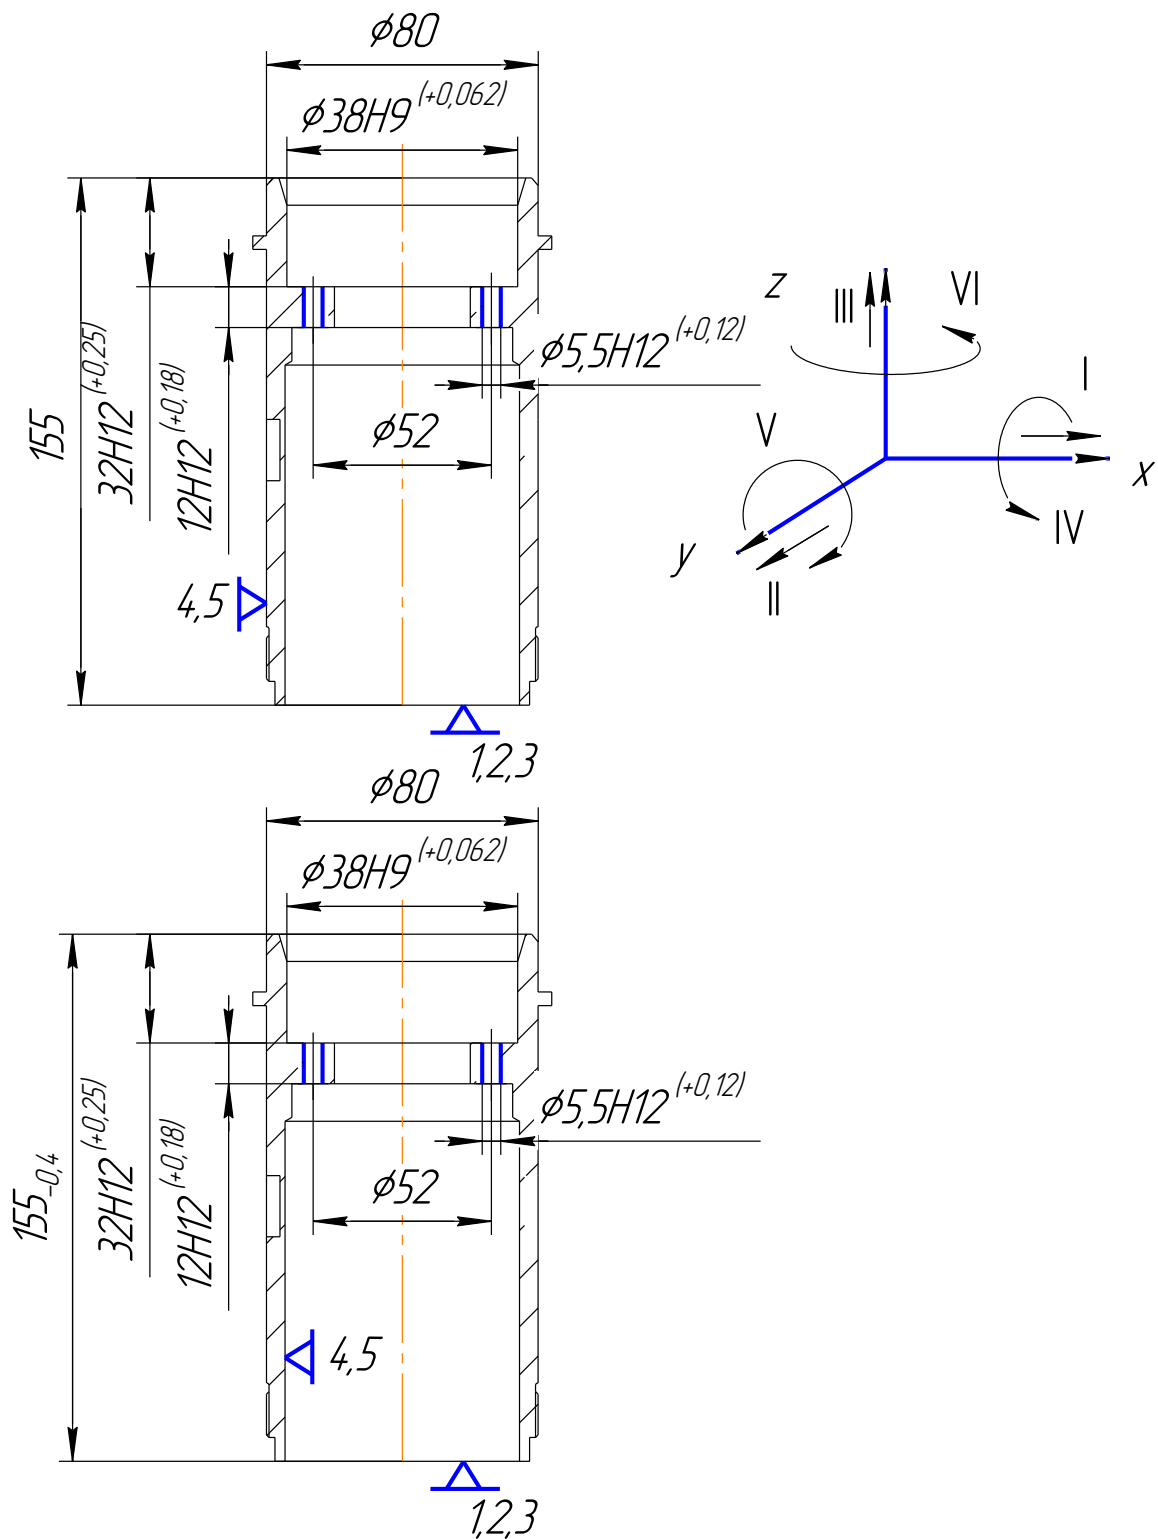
Ескіз закріплення заготовки на операції 025
